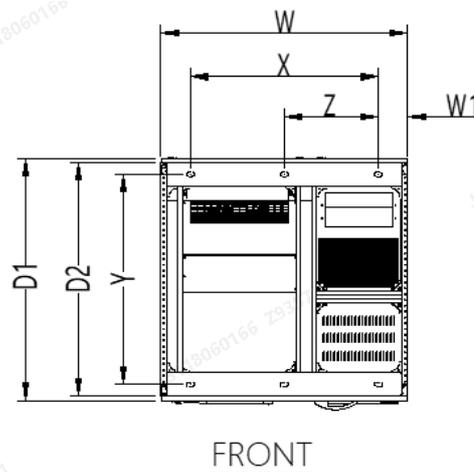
EPK 选件柜底座开孔示意 (单位: mm)
